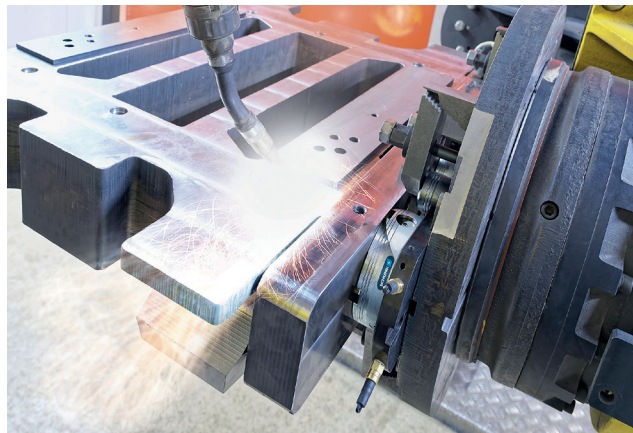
На шарнирном столе сварочного робота MTS также применяется принцип непосредственного зажима с использованием SCHUNK VERO-S, например, для обработки конструкций со всех сторон
